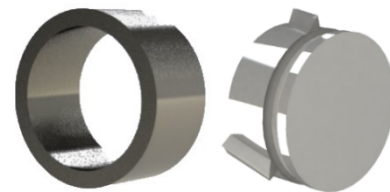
Трехмерная модель участка режущих зубьев протяжки и заготовки
